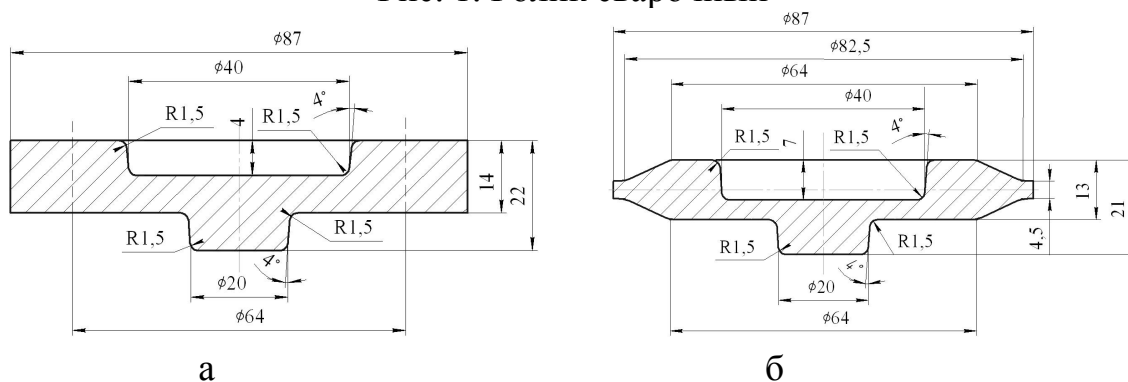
Заготовки детали «ролик сварочный»:
